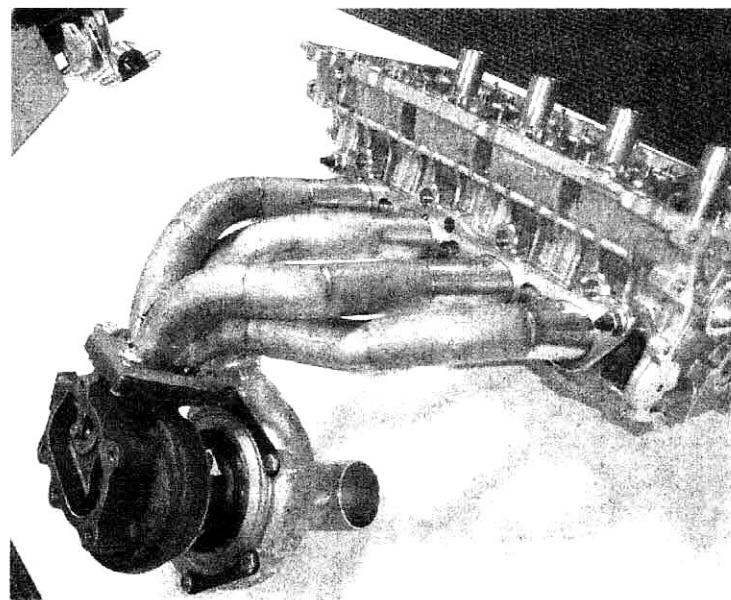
Подгонка деталей для сварки, при формировании выпускного коллектора для Lotus Elise turbo.
